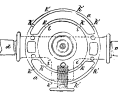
den Grundriß und den Durchschnitt eines dieser Ventile.
